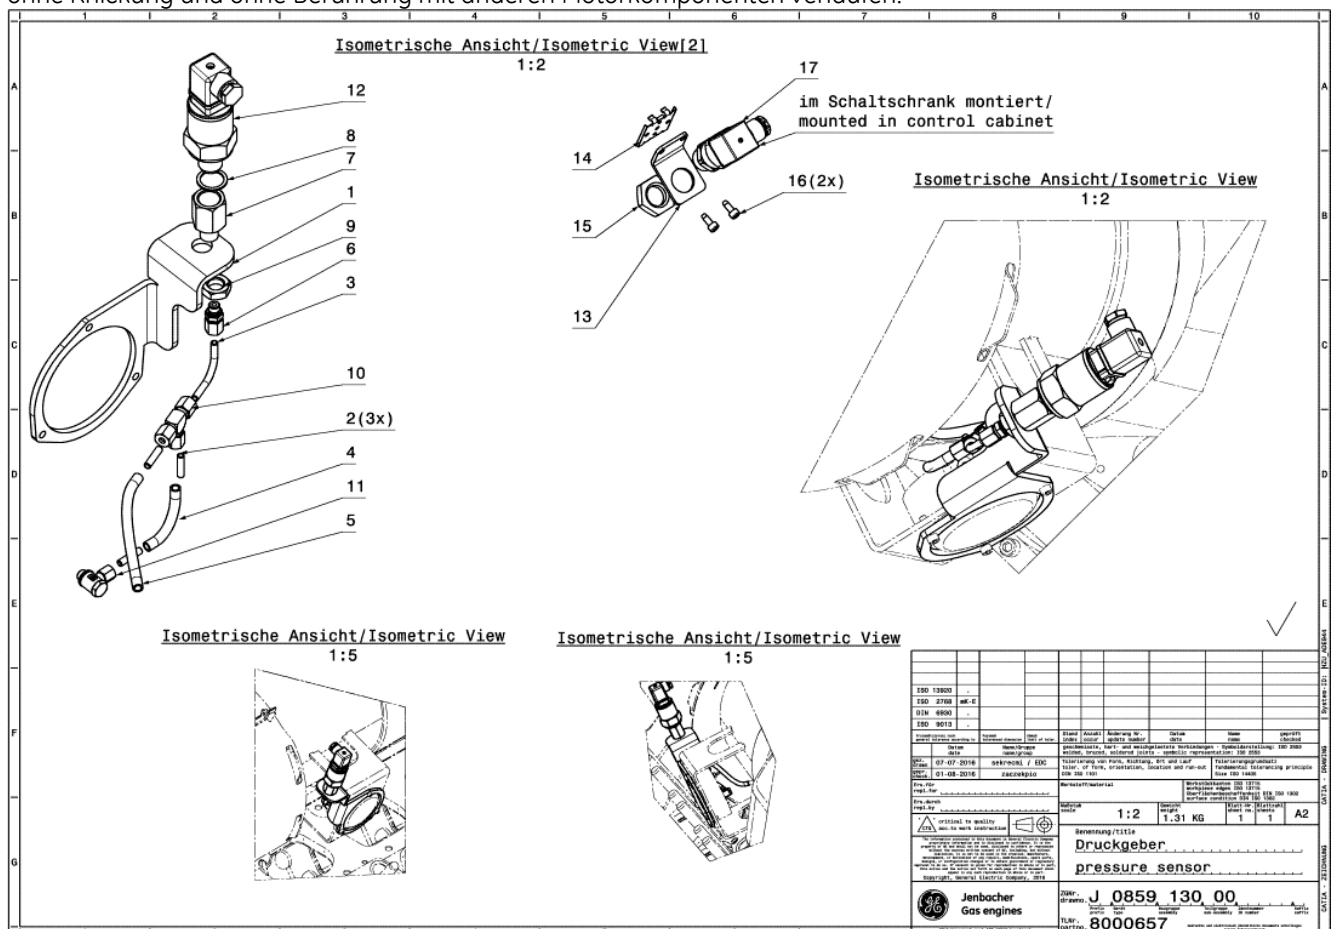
Zeichnung – Luftfilterdruckmodul – TL8000657
